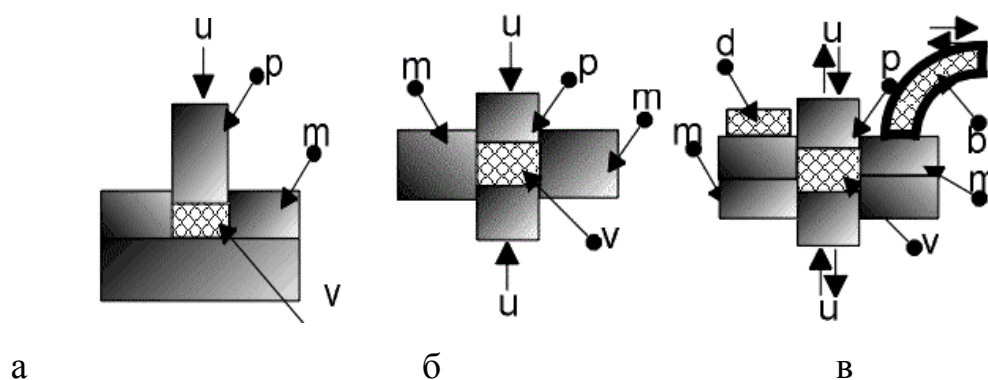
Различные варианты прессования: а – прессование с одним пуансоном; б – прессование с двумя пуансонами; в – прессование с автоматически заполнением пресс-формы и выталкиванием готовой прессовки (u – направление усилия, m – матрица пресс формы, p – пуансон, v – прессуемое вещество (порошок), b - бункер-питатель, d – спрессованная деталь) [7]
